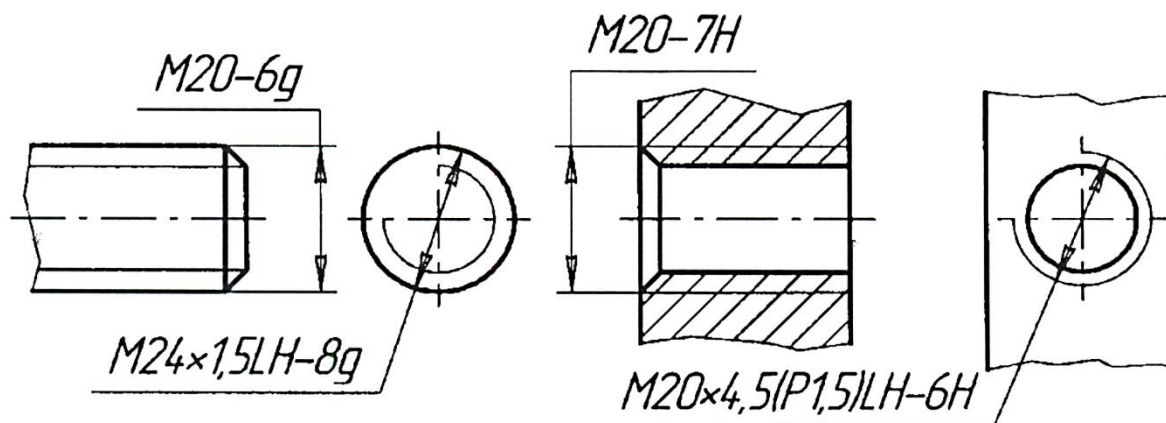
Обозначение метрической резьбы на чертежах
